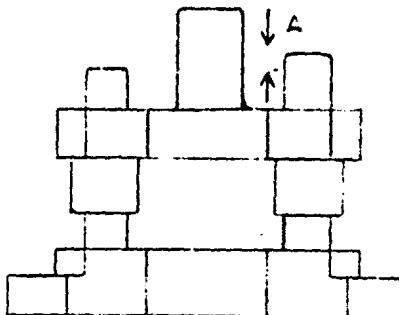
Columnas guías de distintas longitudes para facilitar la colocación de la zapata sup.
